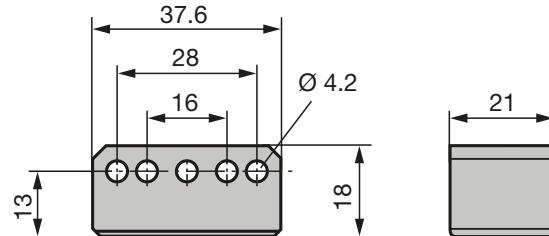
Dimensions de montage du capteur de position BTL6-A-3801-2
